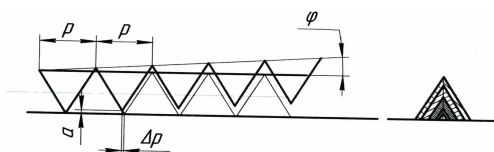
Схема образования профиля резьбы метчика без смещения вершины
